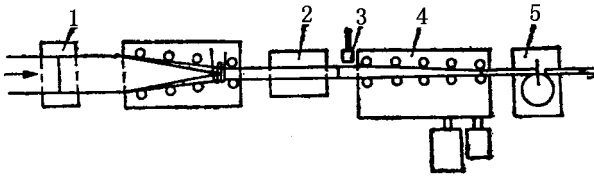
连续焊管机组作业线平面布置示意图
